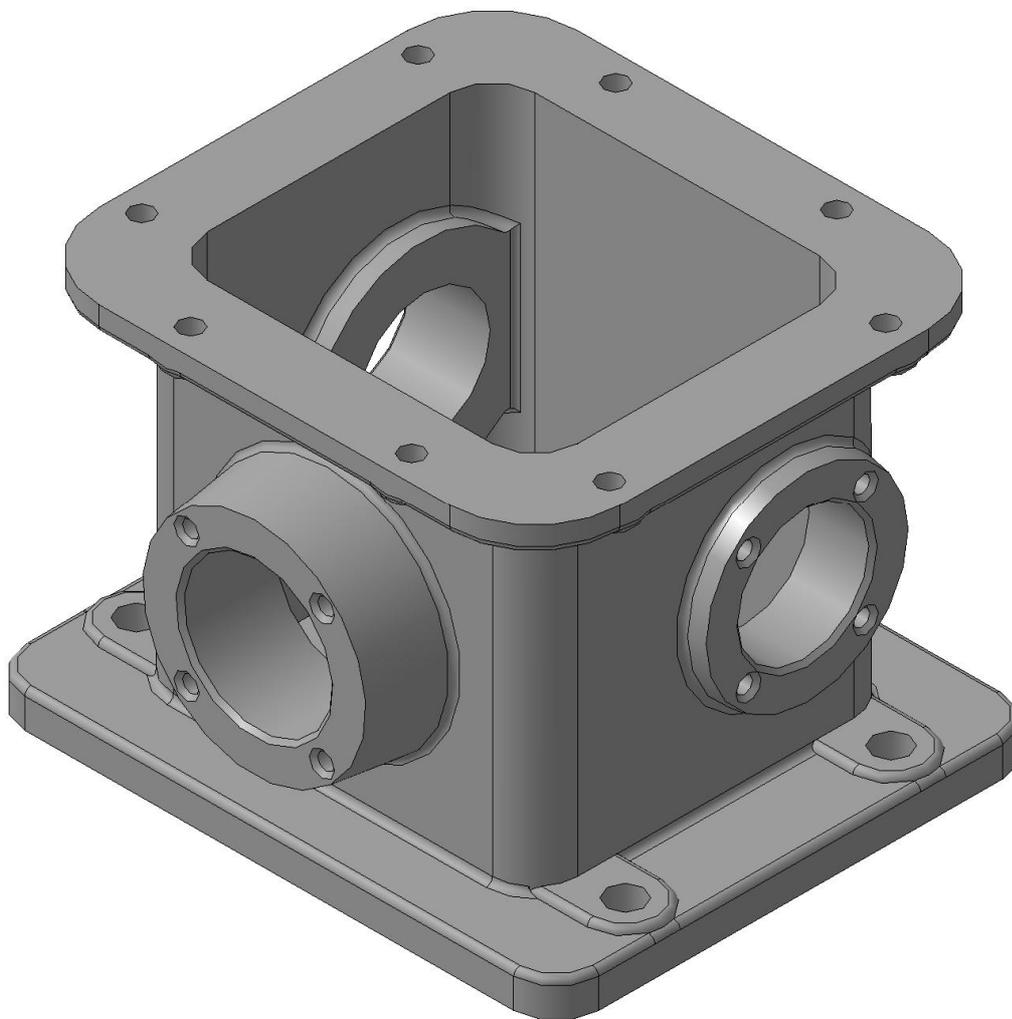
3D-модель детали «Корпус червячного редуктора»
